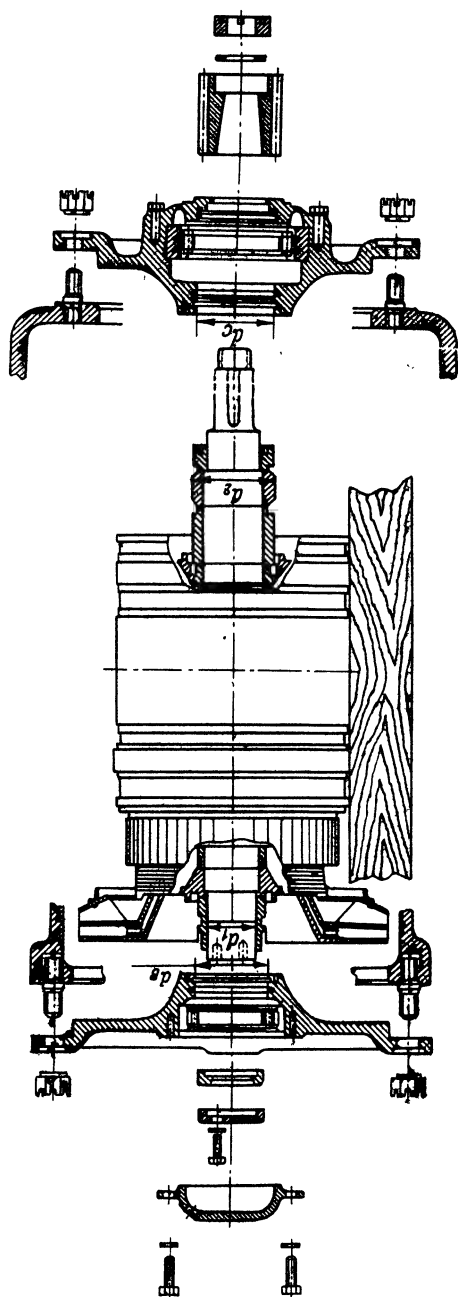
Якорь тягового двигателя со снятыми подшипниковыми щитами
